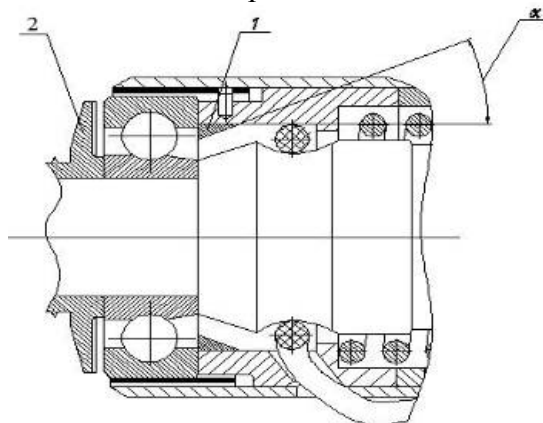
Конструкция подшипникового узла с конической вставкой:
